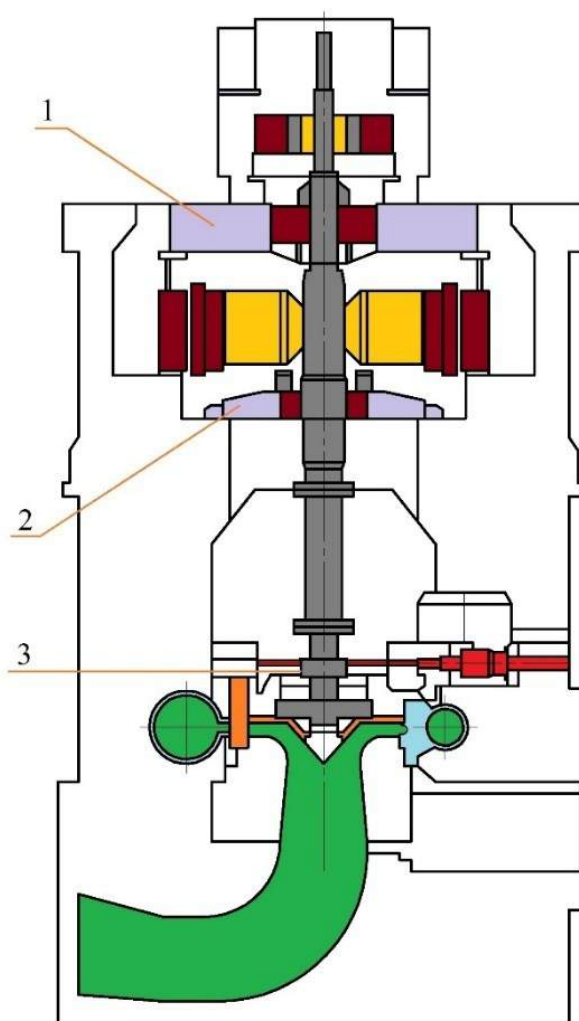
Розташування опор валопроводу гідроагрегату (1 – верхній генераторний підшипник, 2 – нижній генераторний підшипник, 3 – турбінний підшипник)
